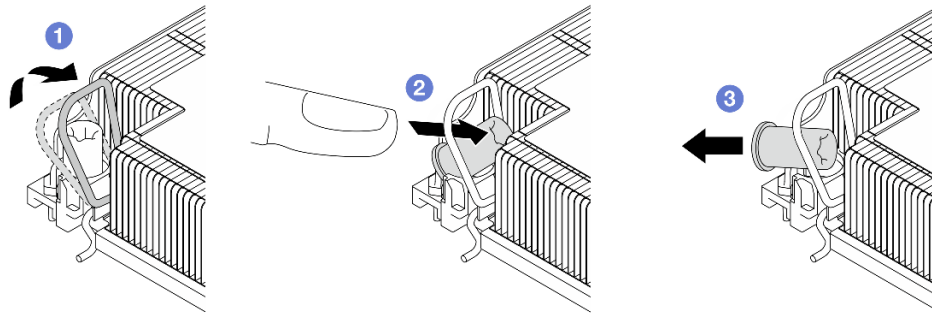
Entfernen einer T30-Torx-Mutter vom Kühlkörper
